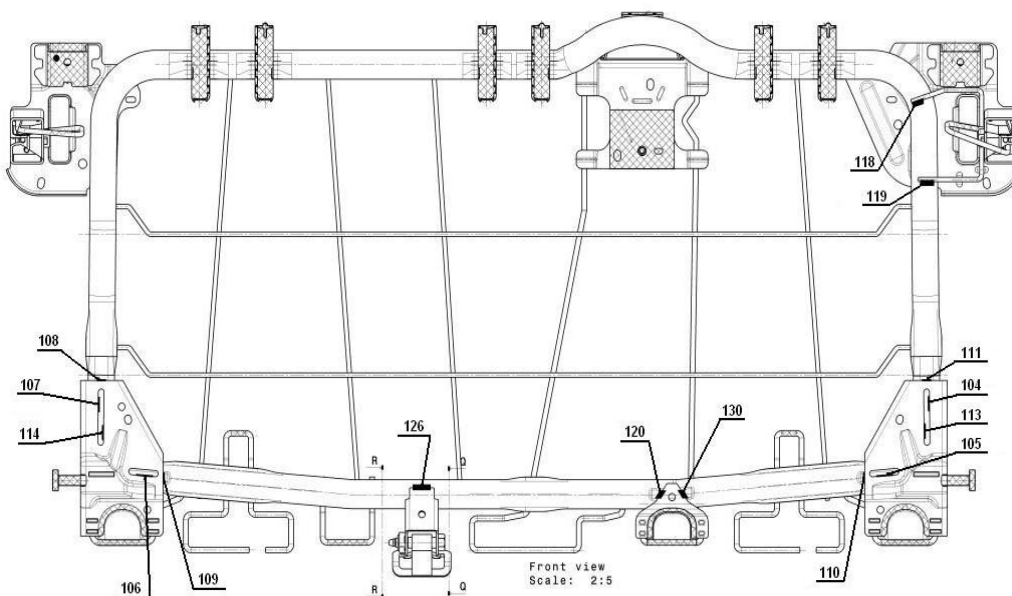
Localização dos cordões de soldadura - Visão frontal
